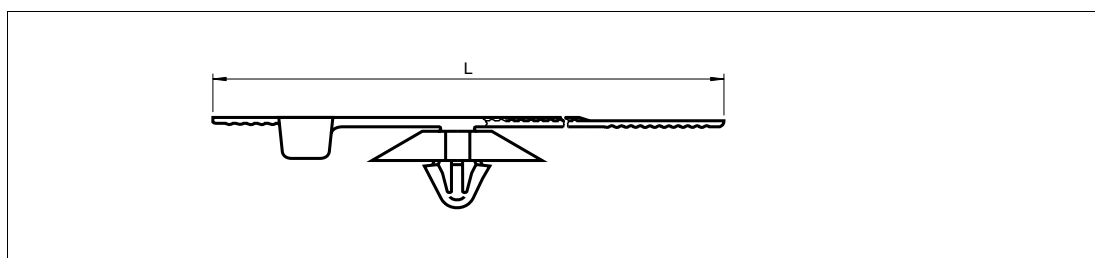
Abmessungszeichnung Kabelbinder
